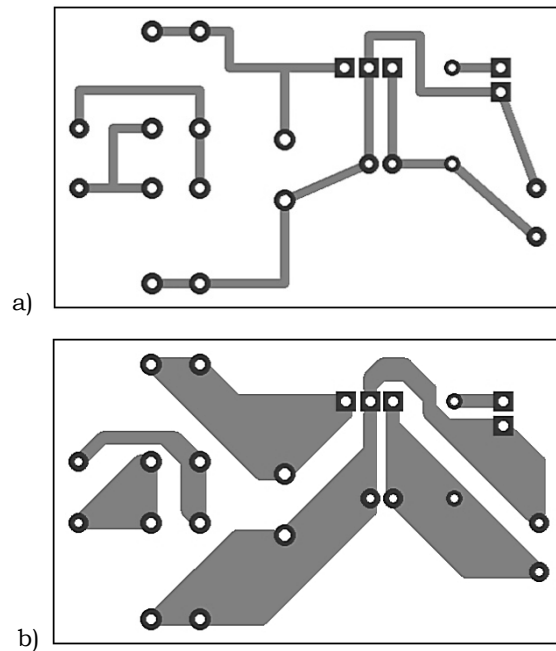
a) PCI com um desenho ruim, b) PCI com um bom desenho.
